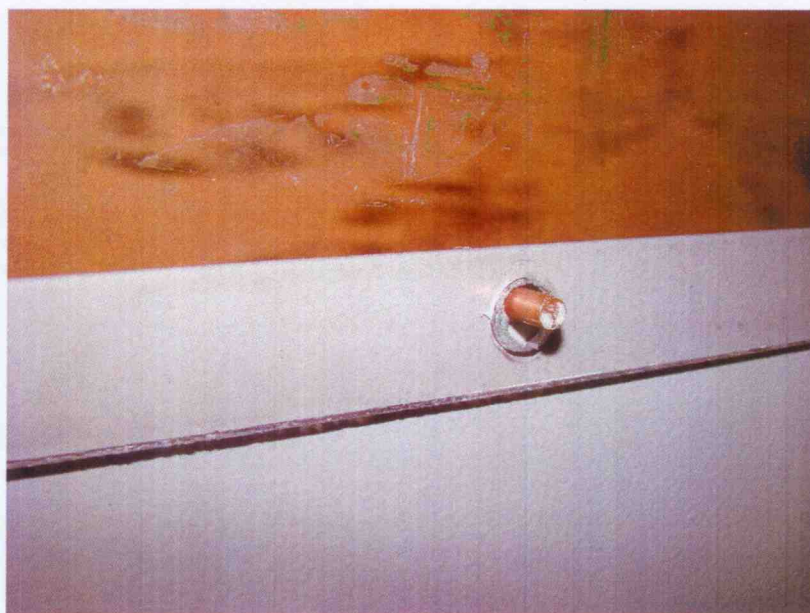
Detalhe do pino para fixação do visor superior da porta frontal após ensaio de impacto
